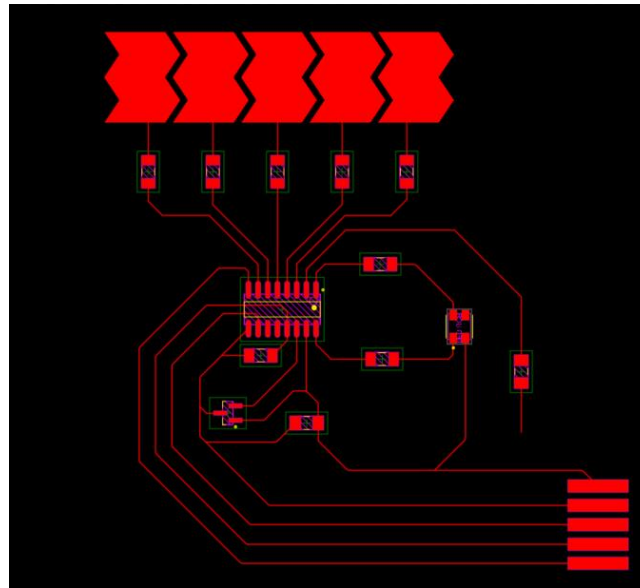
Diseño PCB con grosor de pista de 0,25mm
